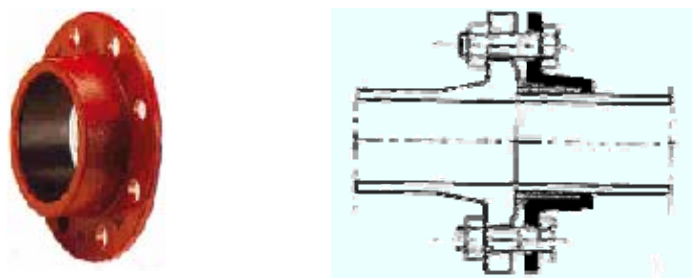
Flanșă și modul de îmbinare a două conducte
